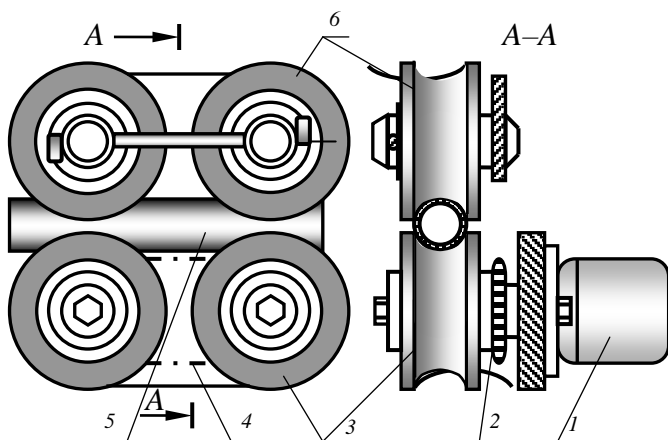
Схема механизма для перемещения напорного шланга: 1 – гидромотор; 2 – ведущая звездочка; 3 – ведущие ролики; 4 – цепная передача; 5 – шланг; 6 – ведомые ролики
